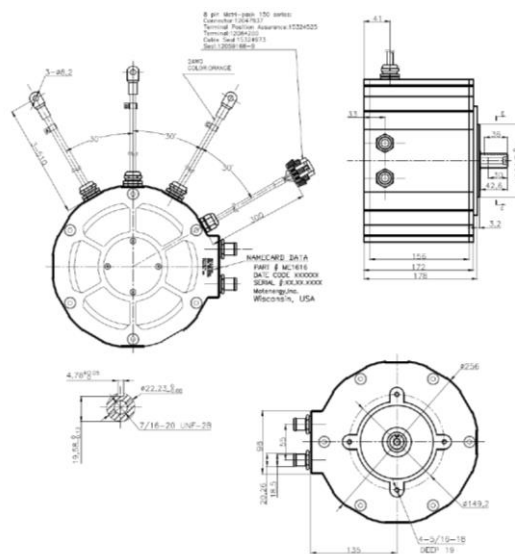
Dimensiones del motor proporcionado por la competición. Fuente www.motostudent.com
